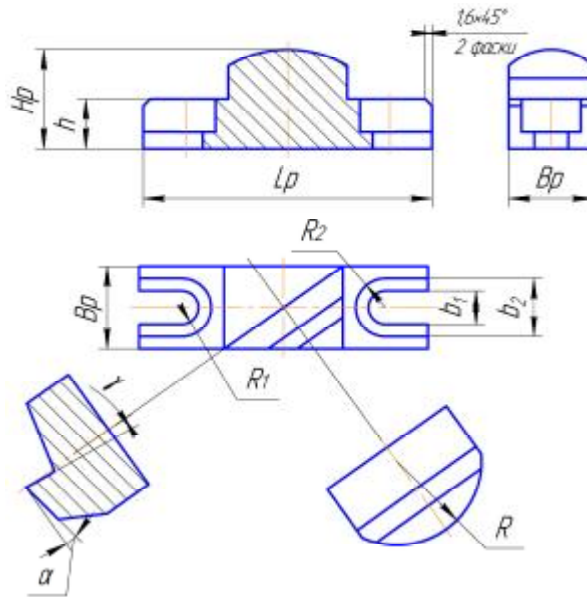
Конструкция вставного зуба-резца, изготовленного из быстрорежущей стали
